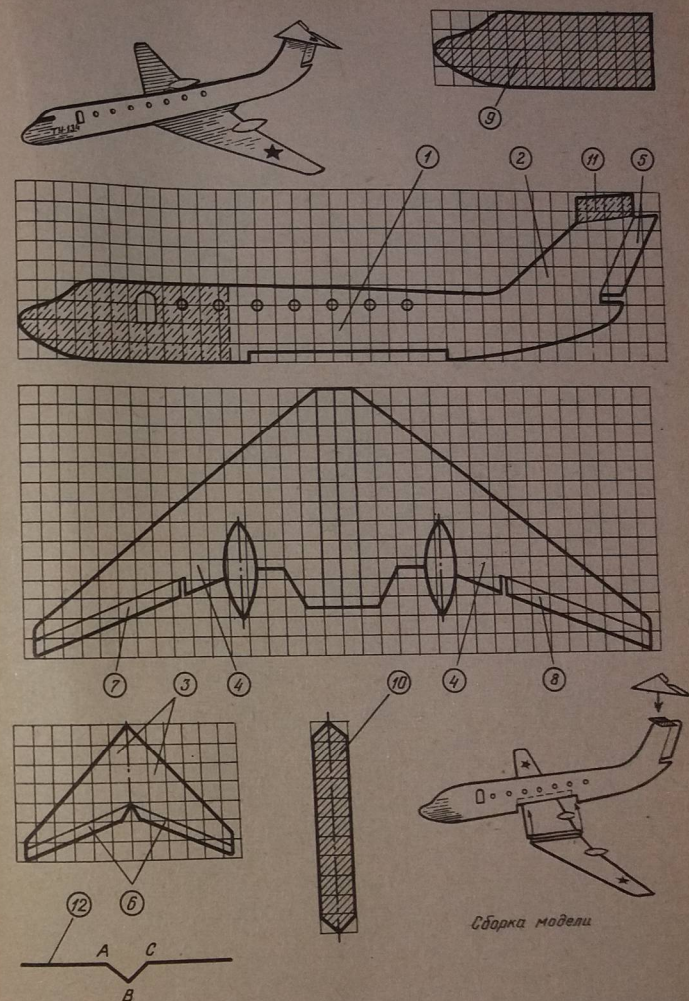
Модель самолета Ту-134: 1—фюзеляж; 2—киль; 3—стабилизаторы; 4—крылья; 5—руль поворота; 6—руль высоты; 7—элерон левый; 8—элерон правый; 9—груз из картона; 10—дополнительная деталь; 11—клапан для клея; 12—схема изгиба крыльев
